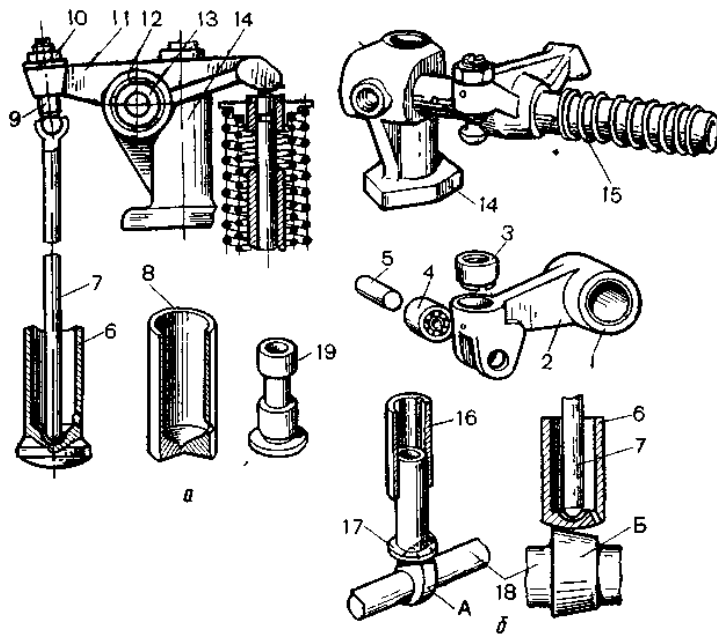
Передавальні деталі газорозподільного механізму (а) і схема повороту штовхачів (б).
